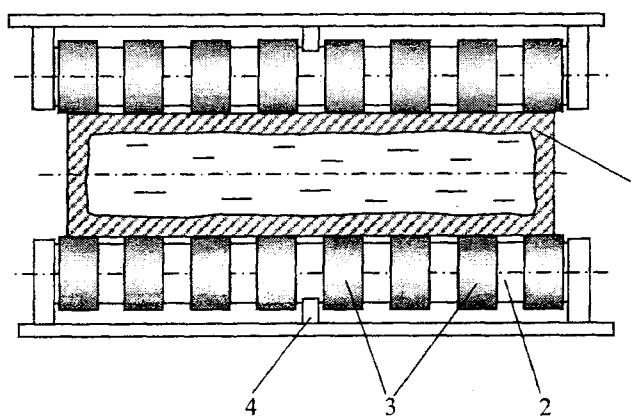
Схема поддержки слябовой заготовки неприводными роликами с неподвижной осью: 1 – сляб; 2 – ось; 3 – ролики;
